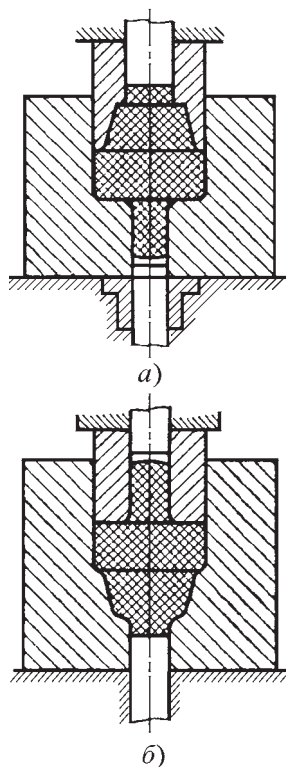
Схемы штамповки поковки со ступенчатой конической головкой:
